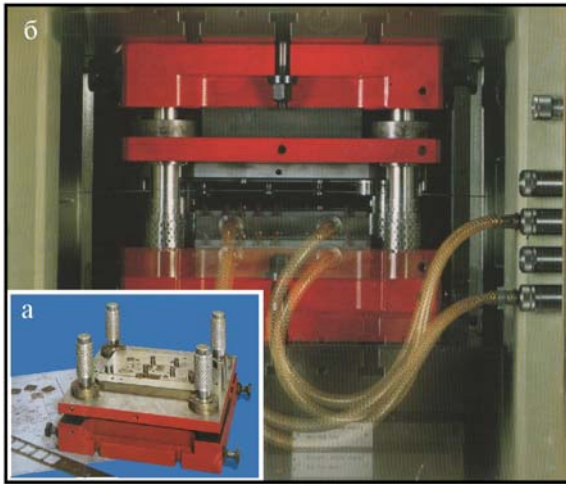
Штамп для чистового вирубання-пробивання: а – нижня частина штампа, штаба та креслення штампа; б – встановлення штампа на пресі-автоматі потрійної дії з гідравлічним приводом фірми Feintool (Швейцарія)
